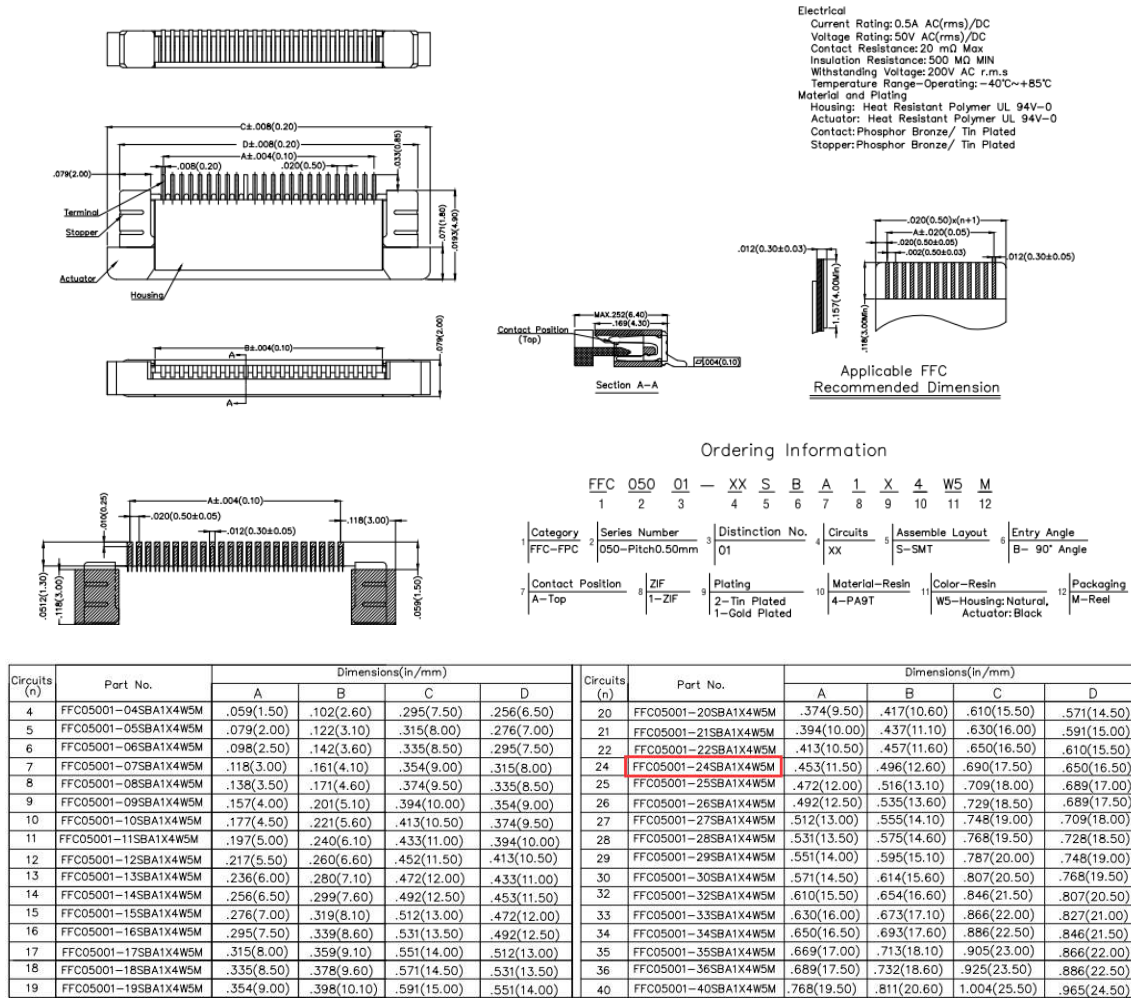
间距 0.5mm 卧式单排 24 PIN PCB 封装
